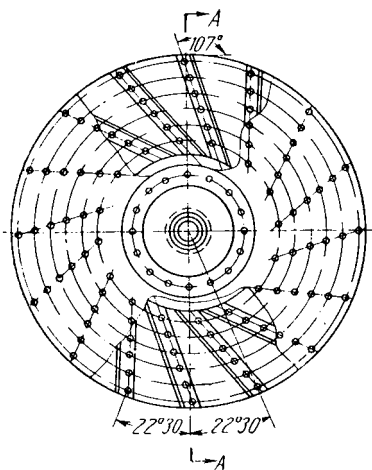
Клепаное колесо вентилятора ВДР с плоскими лопатками
